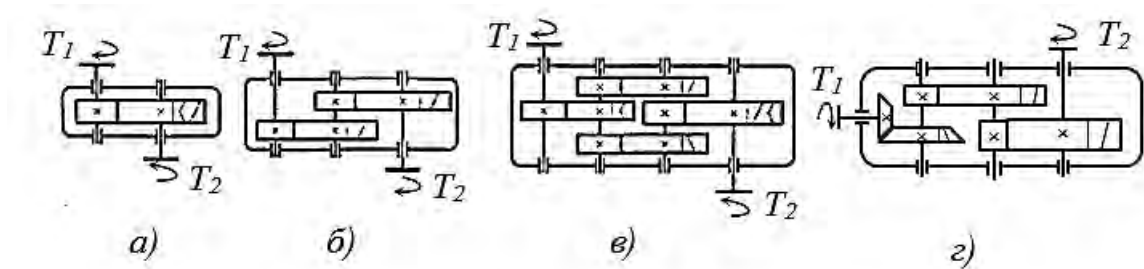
Схеми циліндричного (а,б,в) та комбінованого конічно-циліндричного (г) редукторів.
